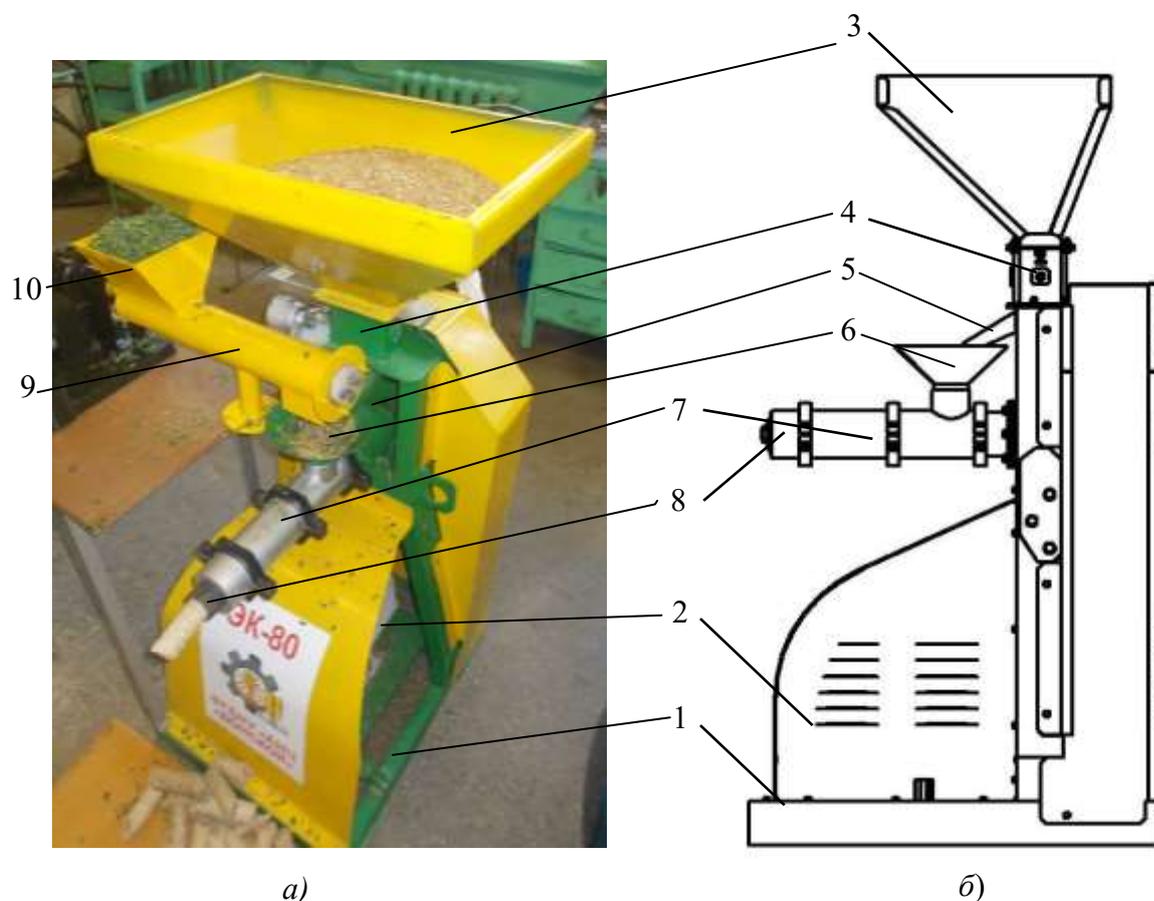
Экструдер кормов ЭК-80 «АНЦ «Донской»: а – общий вид; б – конструктивная схема; 1 – станина; 2 – электропривод; 3 – загрузочный бункер для зерна; 4 – объемный дозатор; 5 – лоток; 6 – сборная воронка; 7 – корпус экструдера; 8 – матрица с фильерой; 9 – шнековый питатель; 10 – загрузочный бункер для зеленой массы
